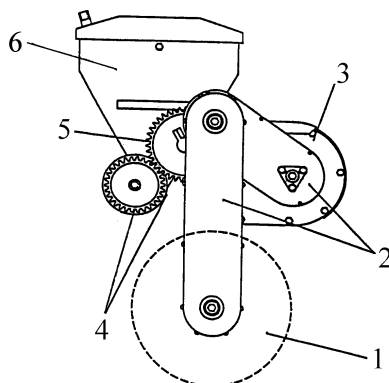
Основные узлы сеялки «Egedal»: 1 – приводное колесо; 2 – цепные передачи; 3 – многоступенчатый редуктор; 4 – двухступенчатая зубчатая передача; 5 – связующая шестерня вала высевающих аппаратов; 6 – бункер
